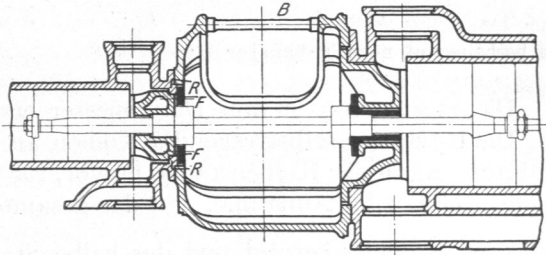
Reihmaschine. Ausbau der Kolbenstange durch den Hochdruckzylinder hindurch.
